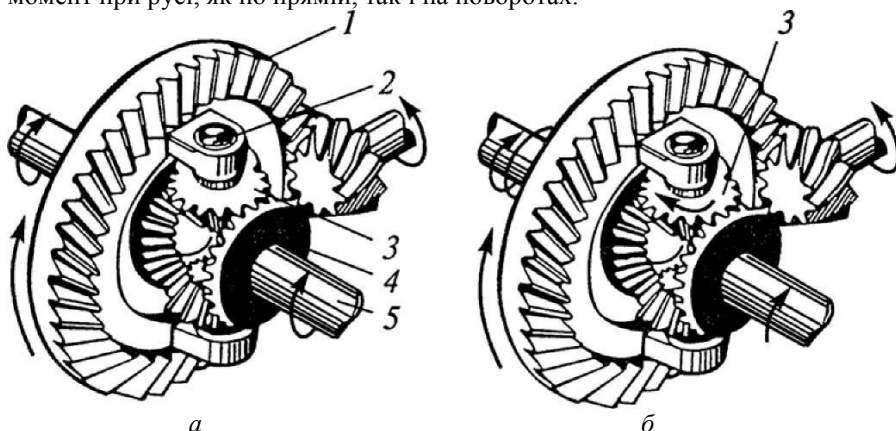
Конструкція і схема роботи конічного диференціала: а - прямолінійний рух; б - на повороті; 1 - ведена шестерня головної передачі з коробкою диференціала; 3 - сателіти; 4 - півосьові шестерні; 5 – півосі.
